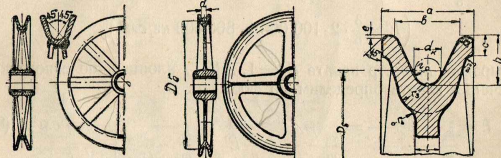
Направляющие блоки для стальных канатов: литые; сварные; профиль канавки блока
